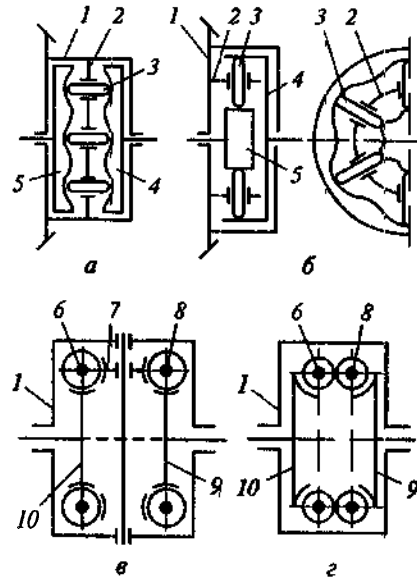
Кулачковые (а, б) и червячные (в, г) дифференциалы: 1 — корпус; 2 — обойма; 3 — сухарь, 4 и 5 — звездочки, 6 и 8 — червяки; 7 — сателлит; 9 и 10 — шестерни
